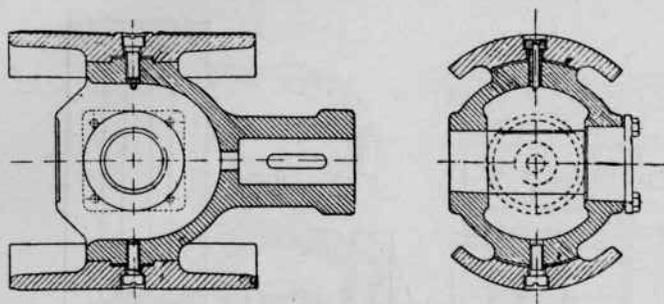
Крепление подставки коленчатого вала к котлу у локомотива СК-4.
